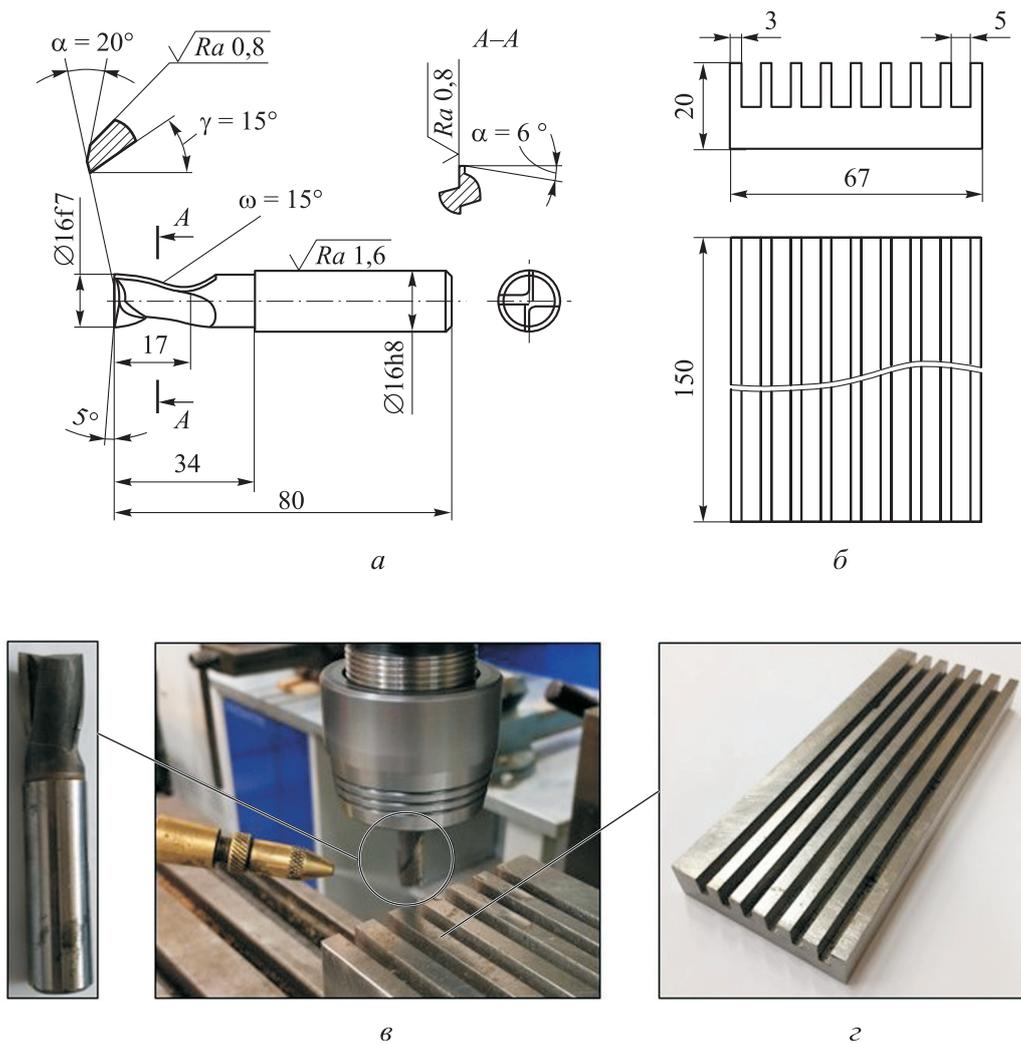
Конструктивные схемы (а, б) и внешний вид (в, з) концевой фрезы (а, в) и обрабатываемой заготовки (б, з)
